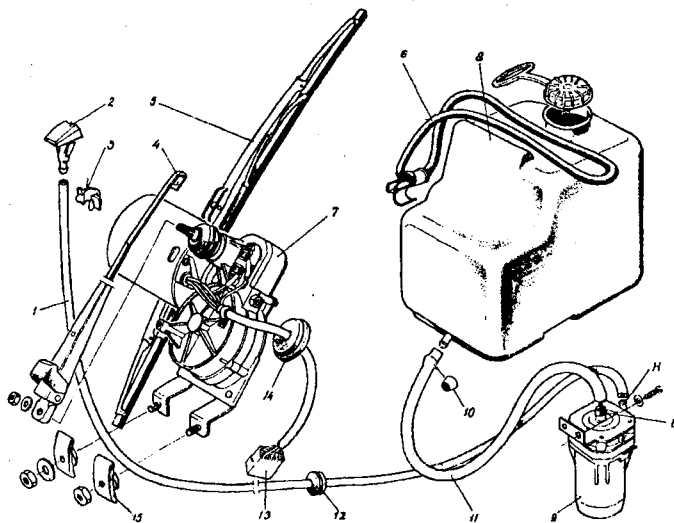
Стеклоочиститель и стеклоомыватель ветрового стекла: 1 – шланг жиклера; 2 – жиклер в сборе; 3 – скоба крепления шланга; 4 – рычаг; 5 – щетка; 6 – держатель бачка; 7 – моторедуктор ветрового стекла; 8 – бачок; 9 – насос; 10 – фильтр; 11 – шланг бачка; 12, 14 – уплотнительная втулка; 13 – штекерные колодки; 15 – дистанционная втулка
